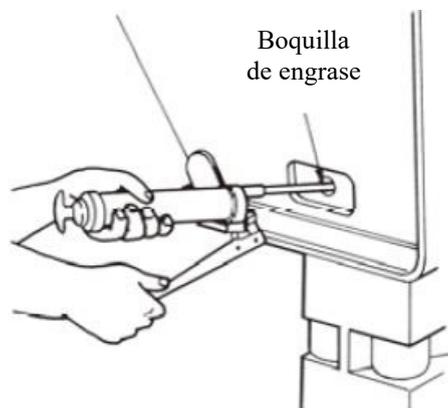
Ejemplo de lubricación con pistola engrasadora
